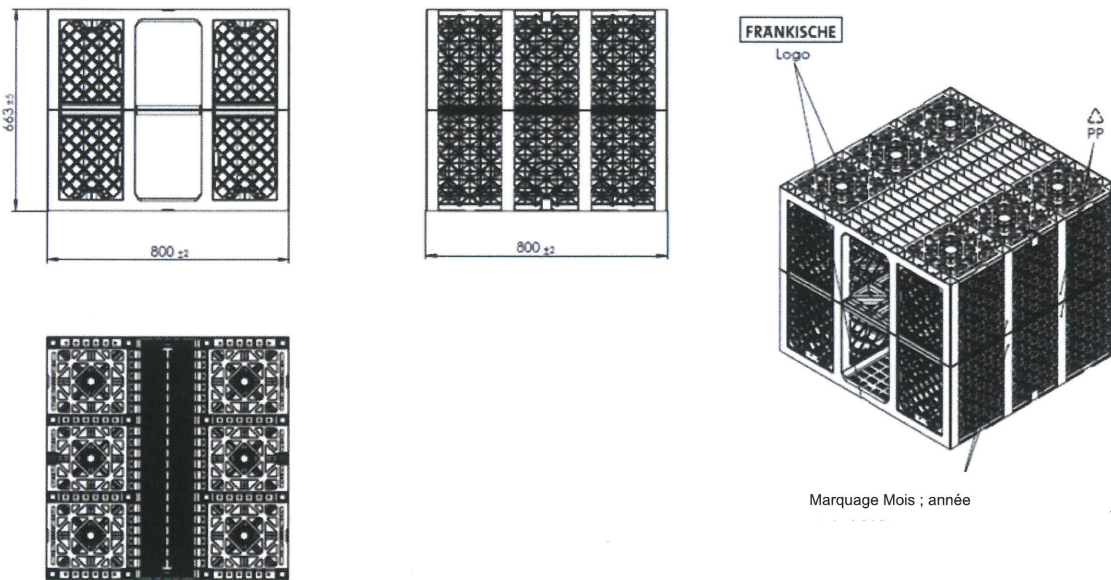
b- Caractéristiques dimensionnelles du module Rigofill inspect
